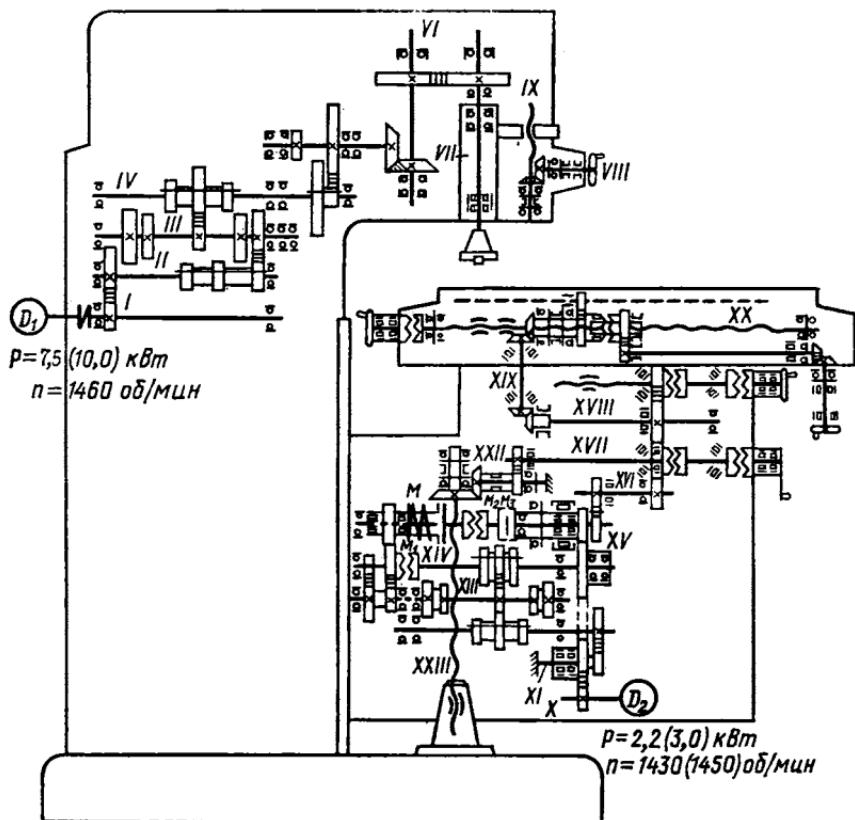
Кинематическая схема фрезерных станков 6Р12 и 6Р13.
